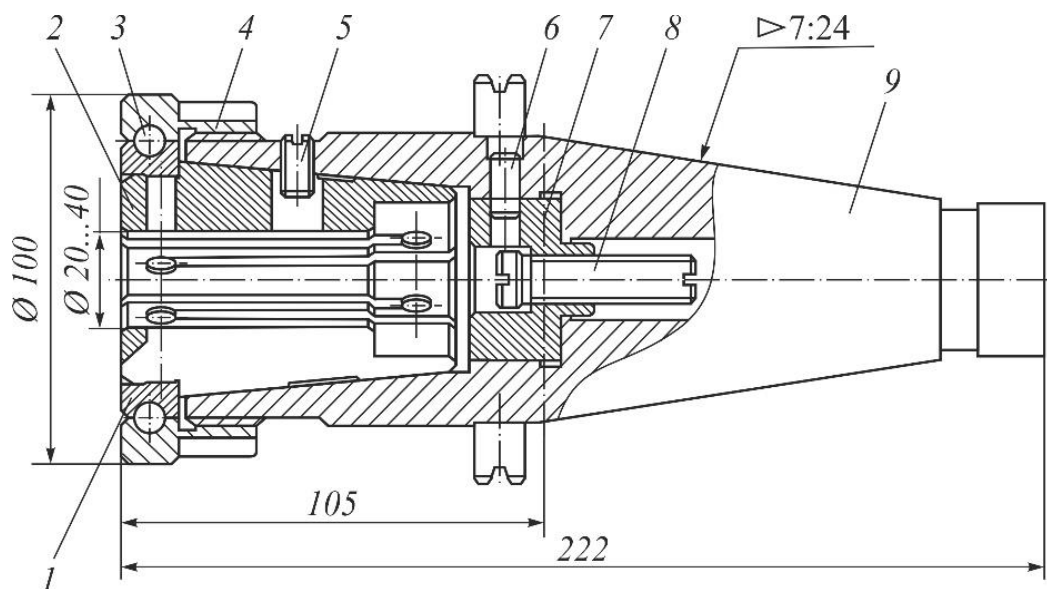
Патрон цанговый с конусом 7:24 для крепления концевых фрез с цилиндрическим хвостовиком диаметрами 20...40 мм
